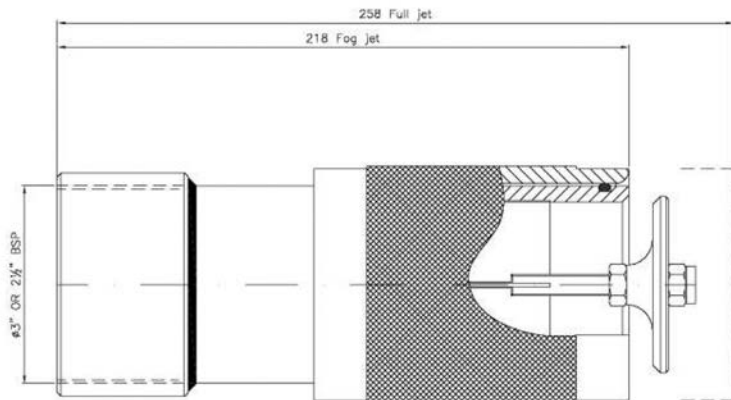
Струйный / распылительный насадок для воды / пены EI-FX
